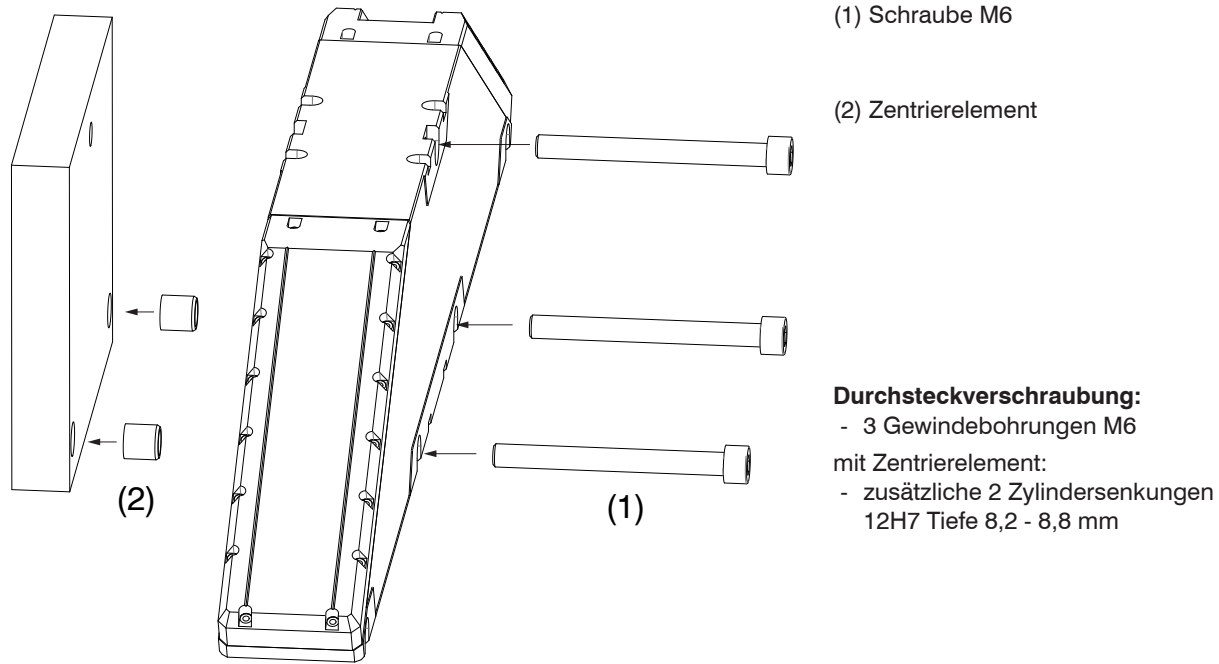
Montagebeispiel Durchsteckverschraubung LLT30xx-430 / LLT30xx-600
